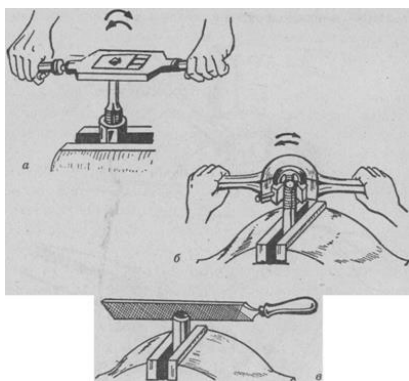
Приемы нарезания резьбы: а — внутренней резьбы с помощью метчика; б, в — опилование торца металлического прутка и нарезание резьбы с помощью плашки и воротка.
